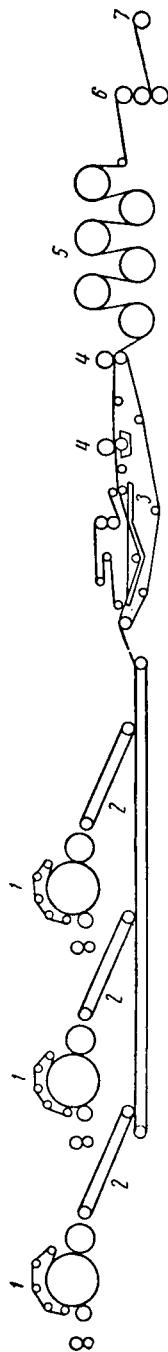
Схема бумагоделательной машины сухого формования с тремя кардочесальными барабанами: 1 — кардочесальный узел; 2 — раскатный валик; 3 — питательный барабан; 4 — зубчатый вал; 5 — приемный барабан; 6 — гибкое кардное полотно; 7 — каландра и накат.
